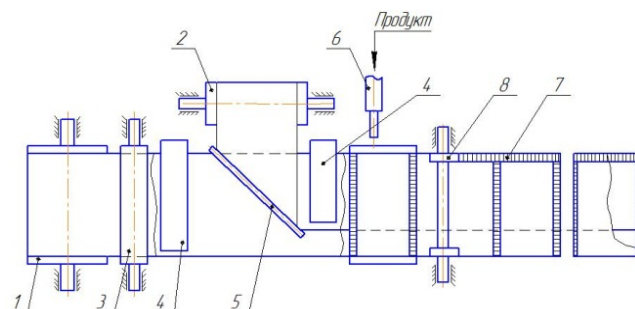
Пристрій для формування двошарової упаковки та заповнення її продуктом
